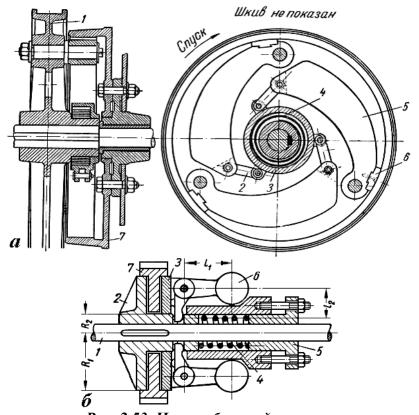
Центробежный тормоз: a - c внутренними колодками; $\delta -$ пластинчатый
